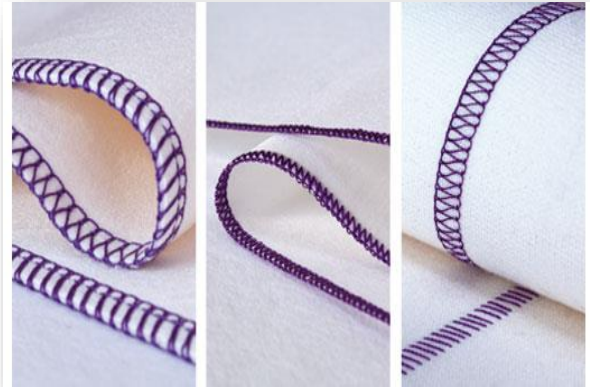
Resultado de máquina remalladora; fuente: Google imágenes
